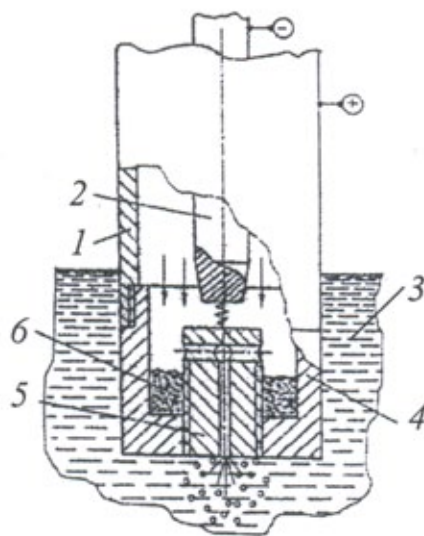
Схема обработки сплавов плазменной струей с парами флюса: 1 – корпус; 2 – подвижный электрод; 3 – жидкий металл; 4 – анод; 5 – сменная вставка; 6 – флюс
